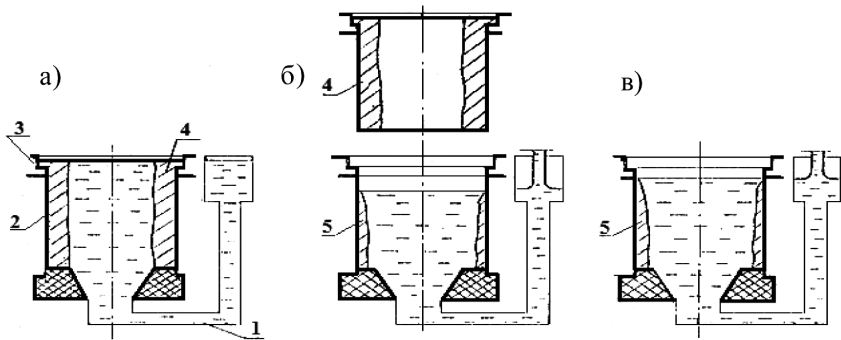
Принципиальная схема литья полых заготовок без стержня: 1 – литниковая система; 2 – стационарный кристаллизатор; 3 – подвижный кристаллизатор; 4 – сформированная отливка; 5 – формирующаяся отливка
